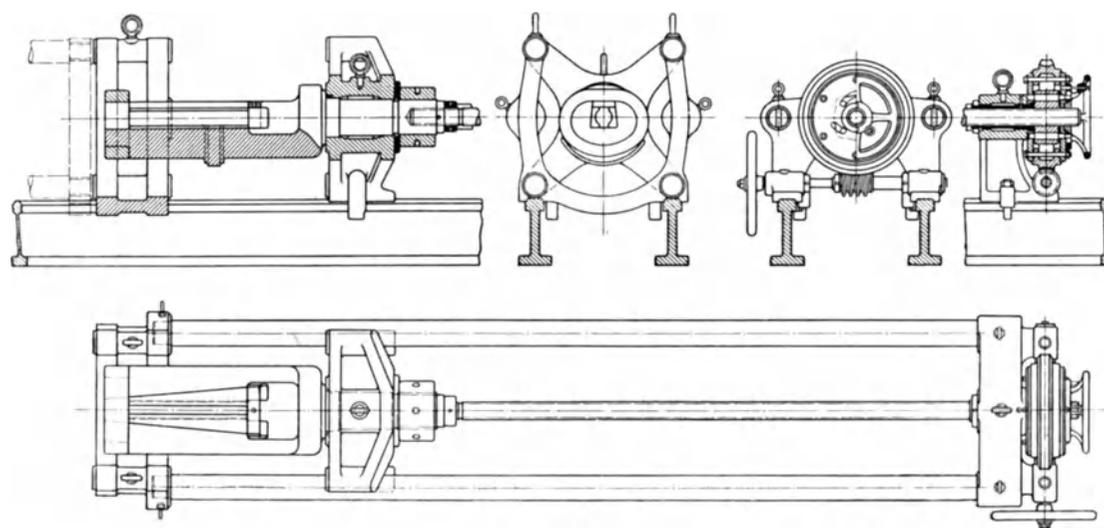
Nachspannvorrichtung für Hanfseile. Maschinenbaugesellschaft Nürnberg.
